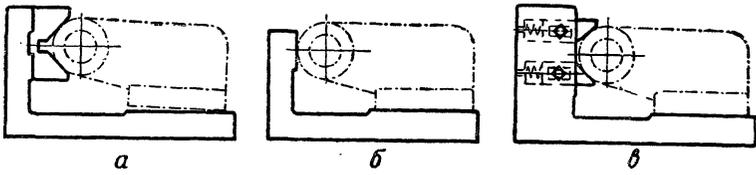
Установка детали с тремя цилиндрическими поверхностями.
